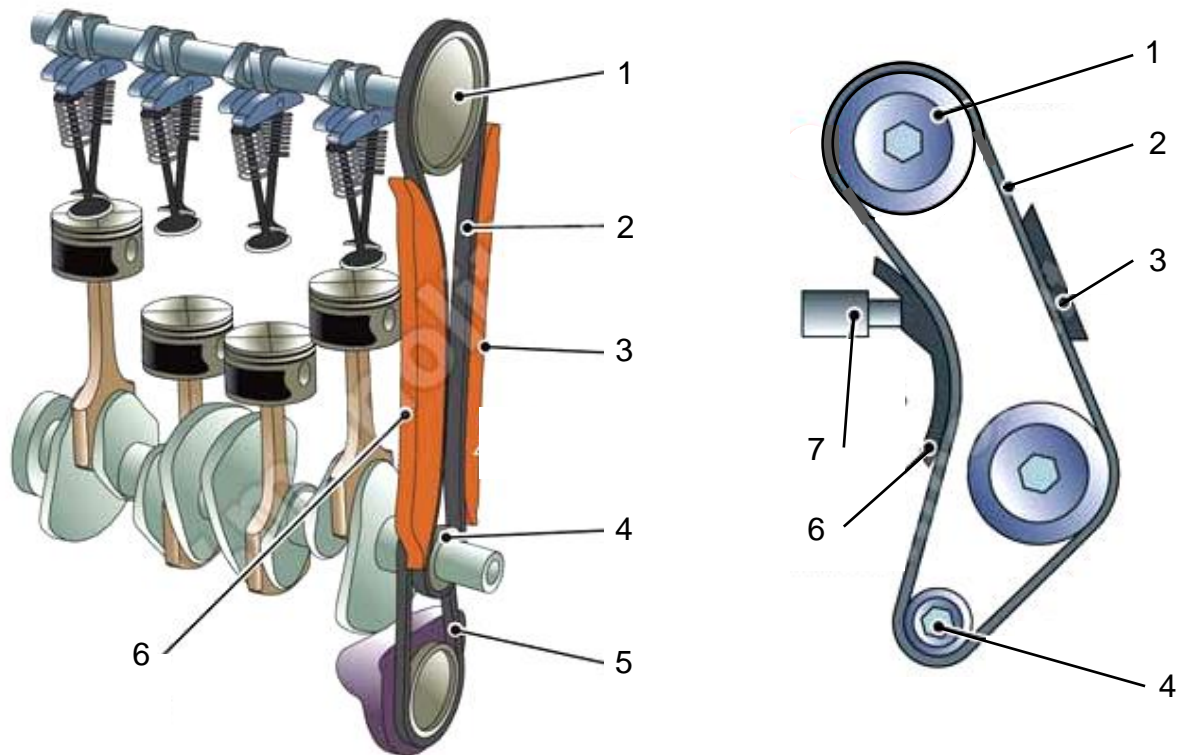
Схема ланцюгового приводу газорозподільного механізму: 1 – зірочка розподільного вала; 2 – ланцюг приводу розподільного вала; 3 – заспокоювач ланцюга; 4 – зірочка колінчастого вала; 5 – ланцюг приводу паливного насоса; 6 – планка натягувала; 7 – натягувач ланцюга
